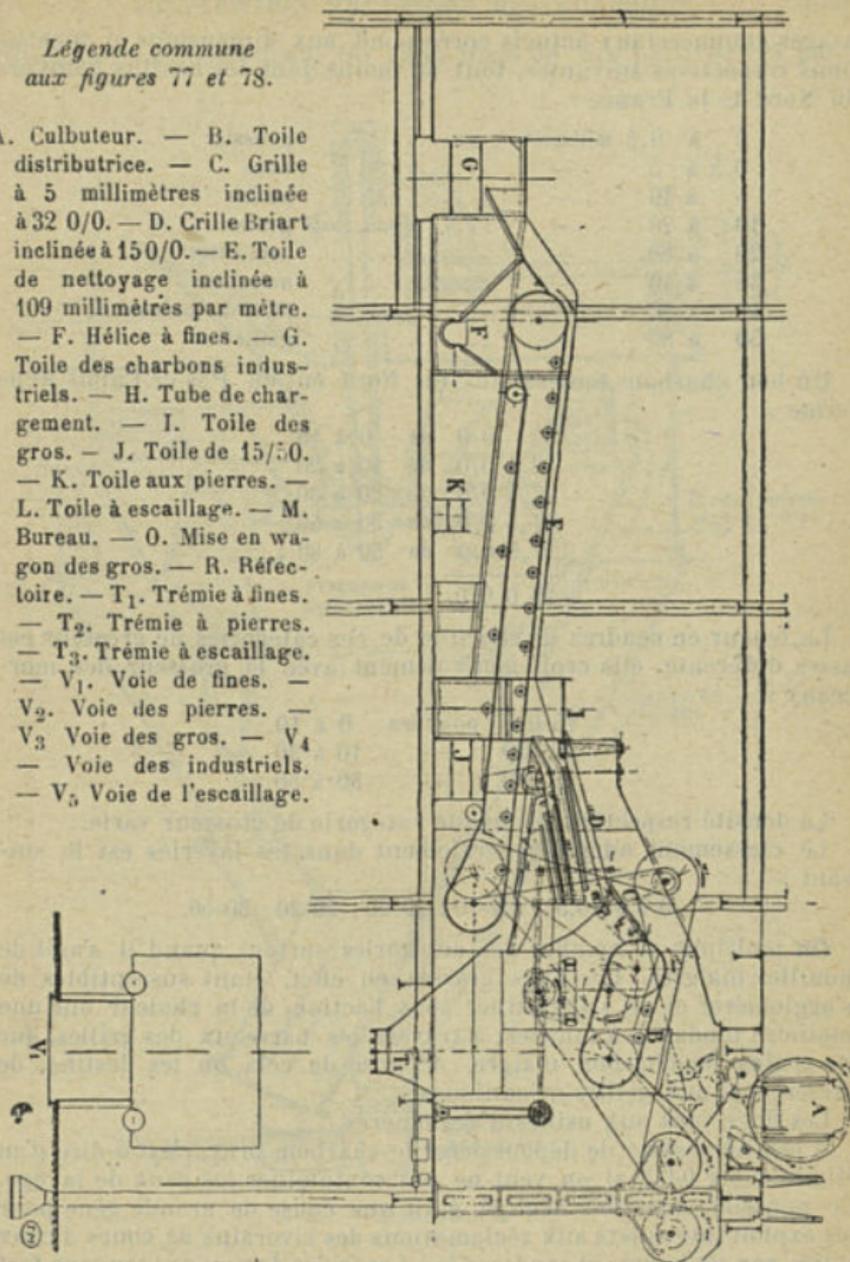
Coupe longitudinale d'un appareil de criblage et de nettoyage de la fosse n° 11 des mines de Lens.
